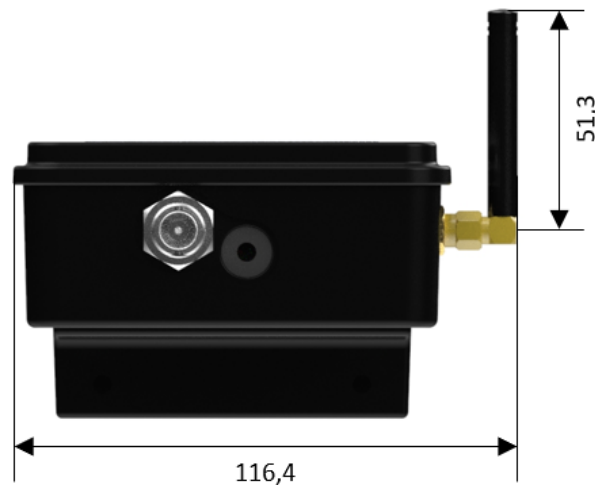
Dimensões [mm] externas do WEGscan400 com presilha para aletas - Vista frontal
